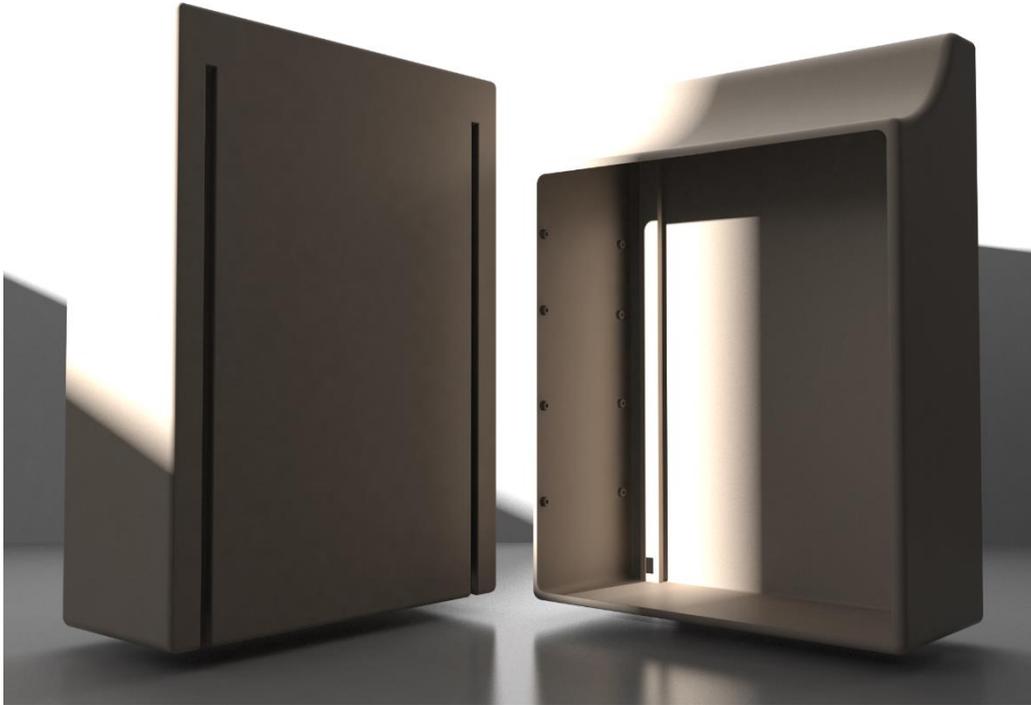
Imagen de la pieza principal con la hembra de la unión.
